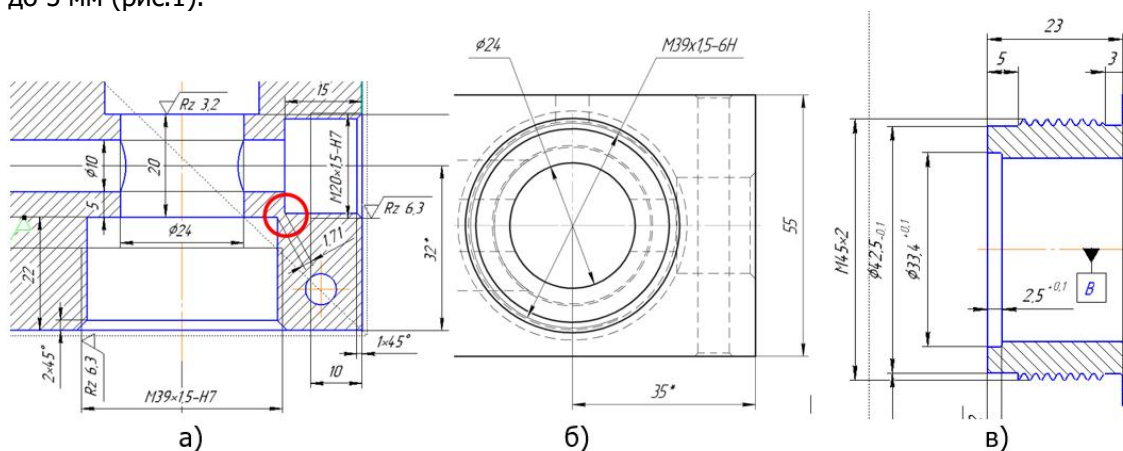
Геометрические параметры резьбового соединения: посадочное место в корпусе; присоединительный элемент датчика
